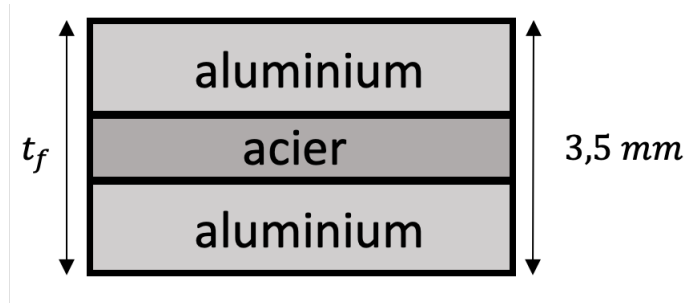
Illustration théorique de la coupe transversale de l'assemblage laminé à 3 couches.
